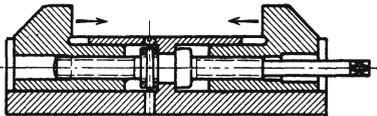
Zwieselschraube mit zwei Hakenmuttern.
